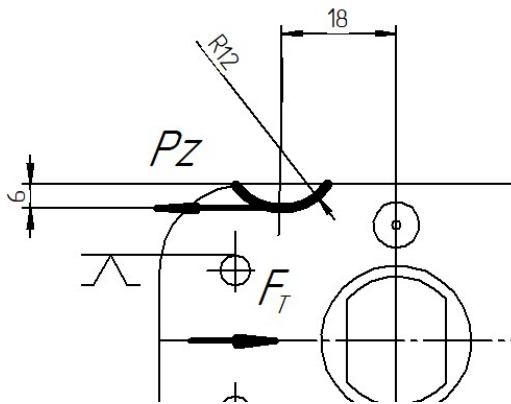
Схема базування та закріплення при фрезеруванні
